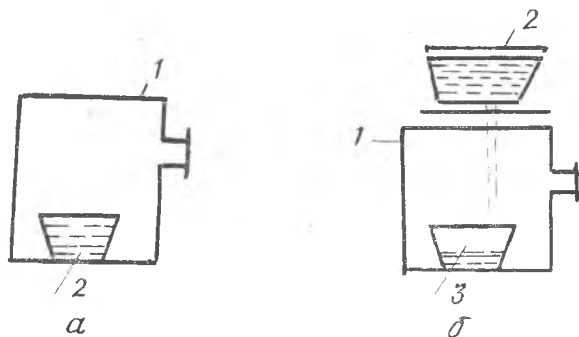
Схемы способов выпечного вакуумирования: а — в ковше, б — в струе металла: 1 — вакуумная камера; 2 — ковш с металлом; 3 — ковш для вакуумированного металла
